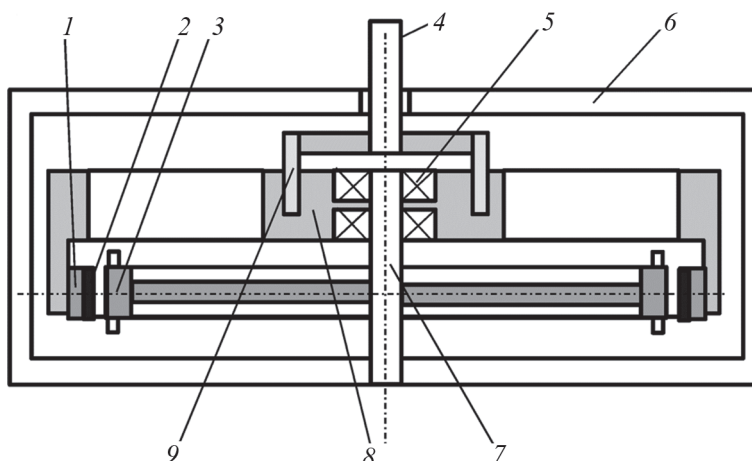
Компоновка тихоходного генератора с внешним ротором на консоли:
